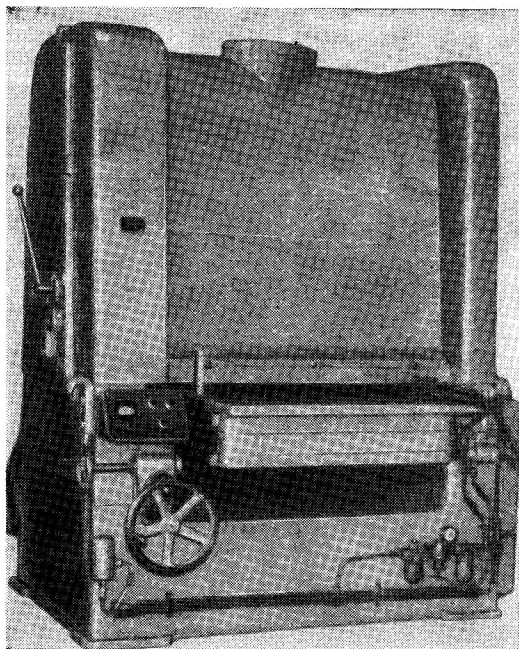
Широколенточный шлифовальный станок ШлК-8
